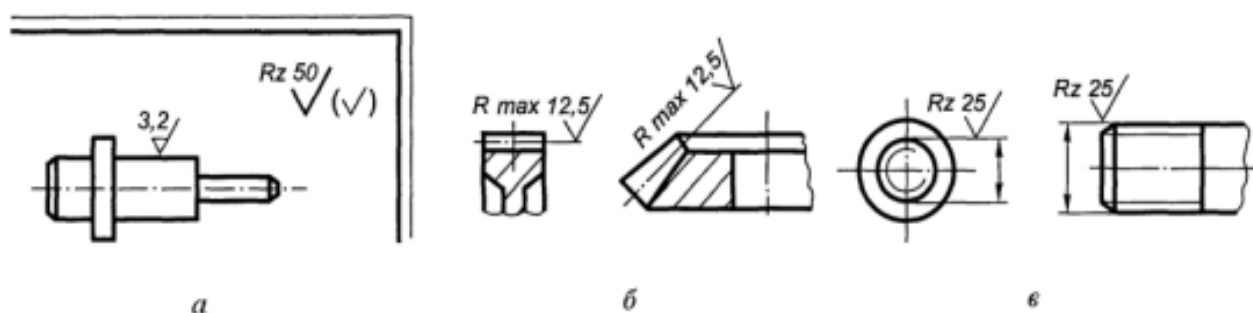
Простановка знака шероховатости: для всего изделия (а), на зубчатое колесо (б), резьбу (в)
